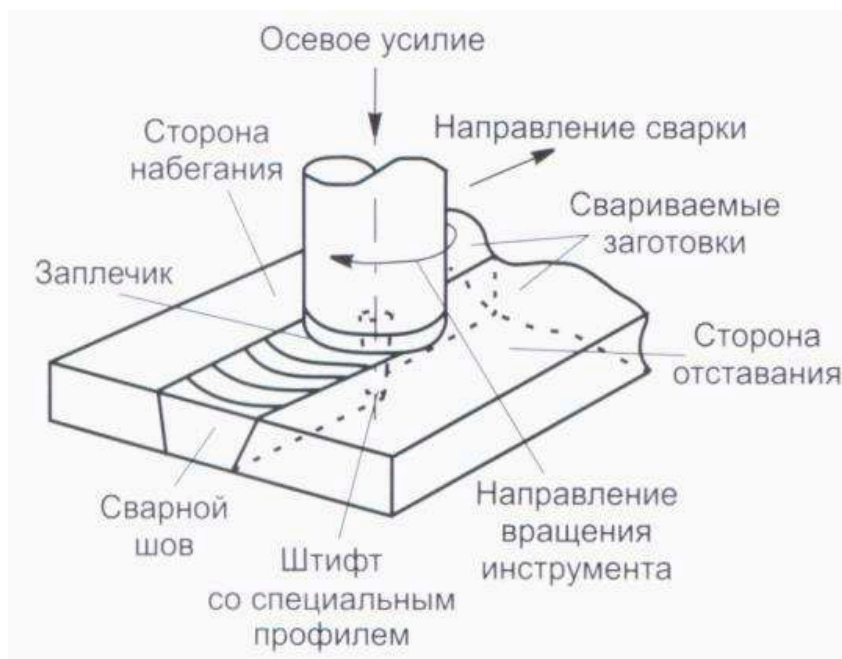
Технологическая схема сварки трением с перемешиванием для выполнения стыковых соединений алюминиевых сплавов [60]
